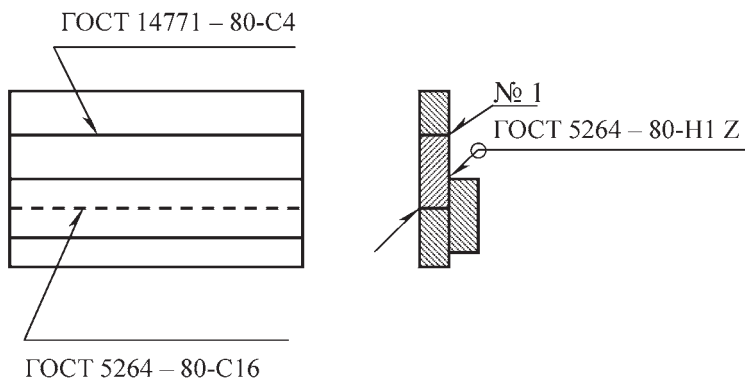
Примеры обозначения сварных швов на чертежах
